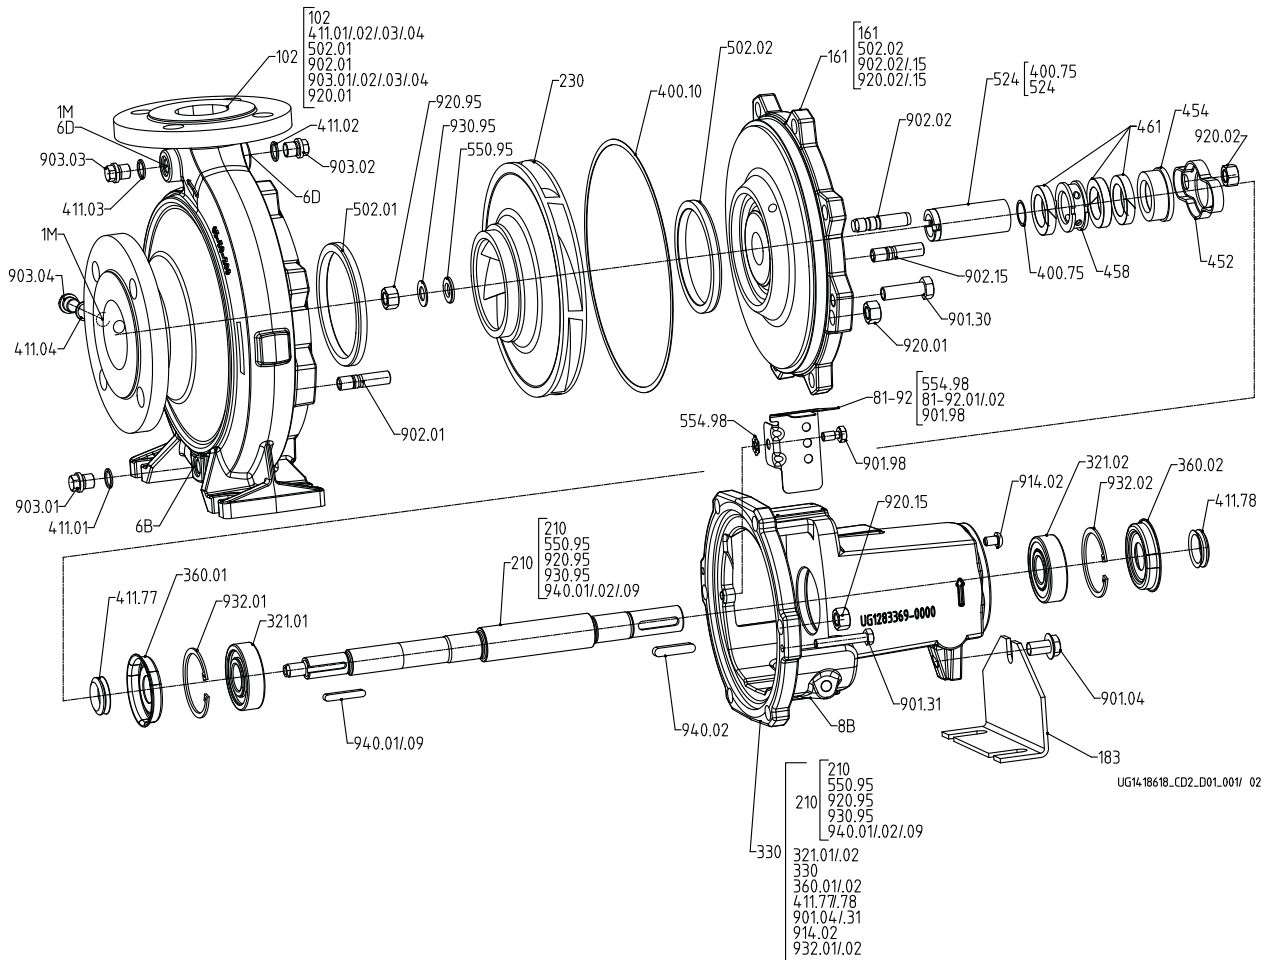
Ausführung mit Stopfbuchspackung und geschraubtem Gehäusedeckel
